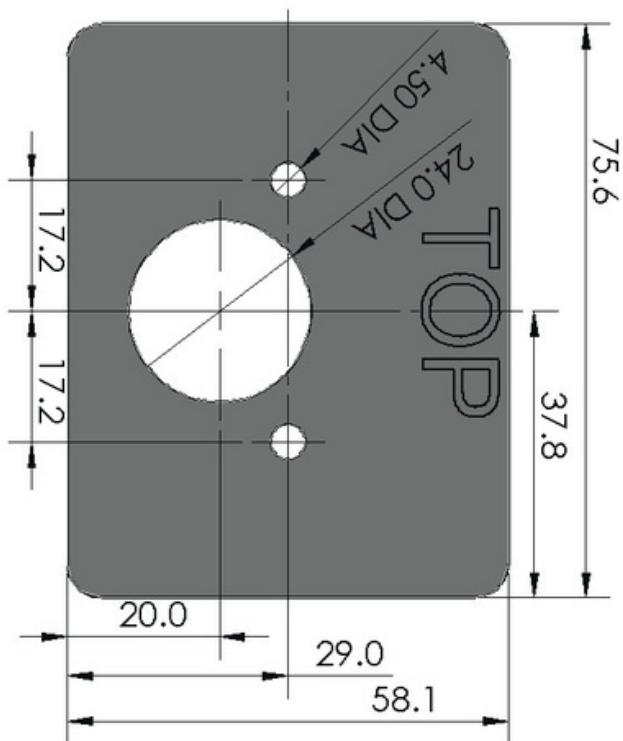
Dimensões dos Furos da Placa de Fixação (mm)
